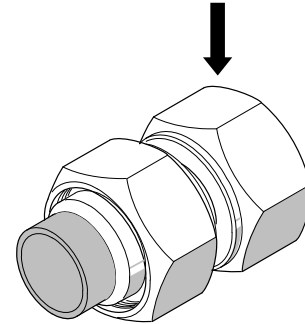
Instale el extremo opuesto a la conexión terminal de adaptador de tubo
